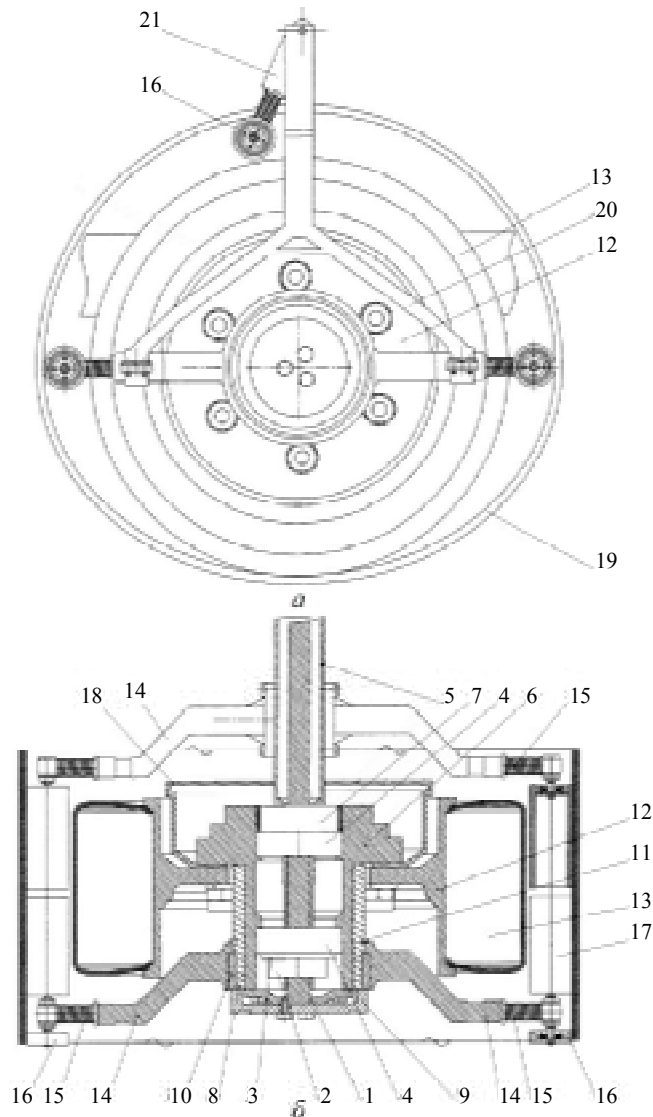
Транспортний засіб з гнучким бандажем, вигляд збоку (а), зверху (б): 1 — фланець півосі; 2 — гайка; 3 — замкова шайба; 4 — конічні роликові підшипники; 5 — картер півосі; 6 — маточина; 7 — мандріжета; 8 — втулка; 9 — кришка втулки; 10 — підшипник ковзання; 11 — кільце стопорне; 12 — диск; 13 — Шина; 14 — реактивні важелі; 15 — пружини стискування; 16 — малі ролики натягування; 17 — великі ролики натягування; 18 — барабан гальмівний; 19 — гнучкий бандаж; 20 — кронштейн; 21 — реактивний важіль маятникового типу
